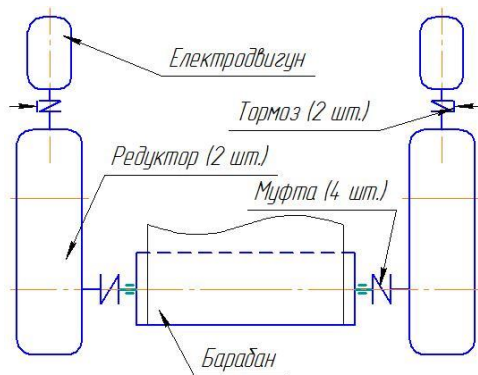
Схема приводної станції стрічкового конвеєра
